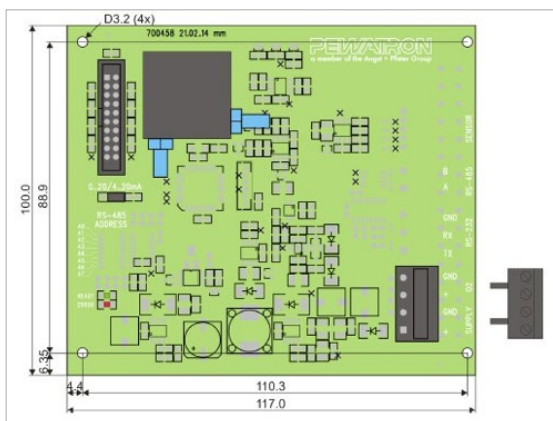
FCX-MCxx-FLOW 模组的 PCB 电子布局
